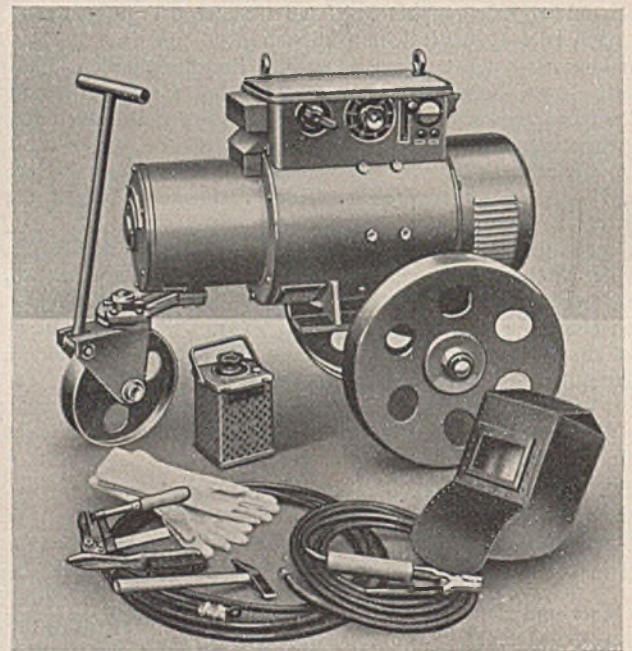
Streufeld-Schweißumformer von Messer & Co., G. m. b. H., der nach dem Grundsatz der „magnetischen Weiche“ gebaut ist.
